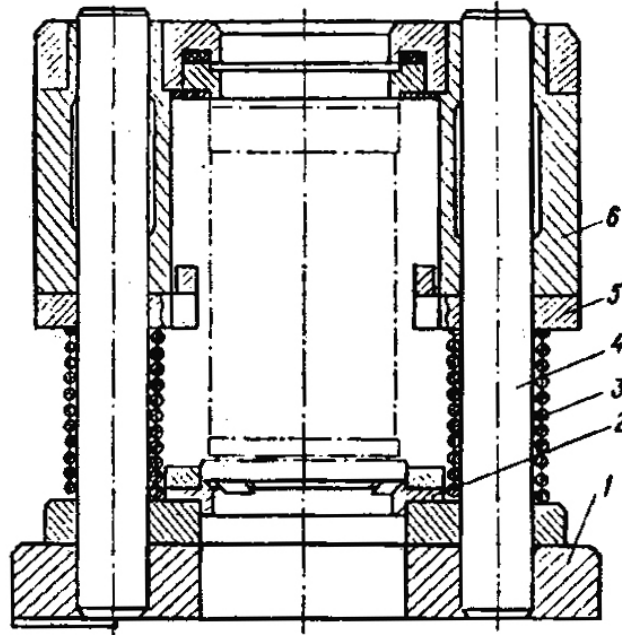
Затискний пристрій для встановлення гільзи циліндра під час розточування: 1 – станина; 2 – упорне кільце; 3 – пружина; 4 – напрямна колонка; 5 – шип; 6 – напрямна втулка
